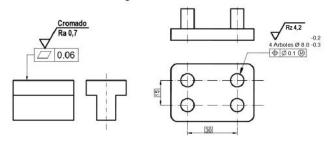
Requisito de calidad superficial sobre la tolerancia geométrica.
